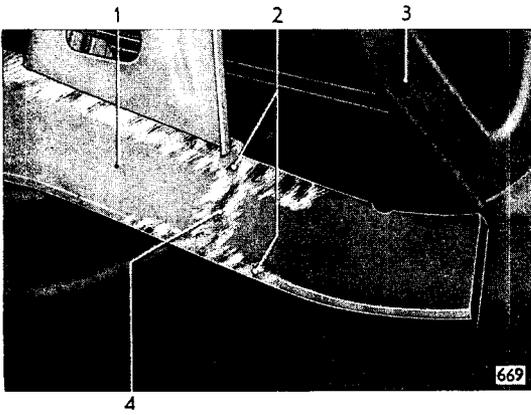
Seitenstrebenflansche beiderseits blankgesäubert und Lichtbogenschweißnaht abgeschliffen
